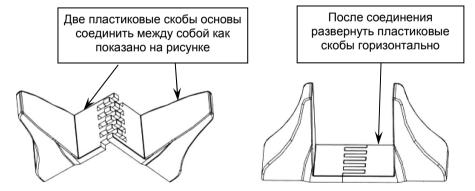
Сборка пластиковых основ для вертикальной установки изделия.
